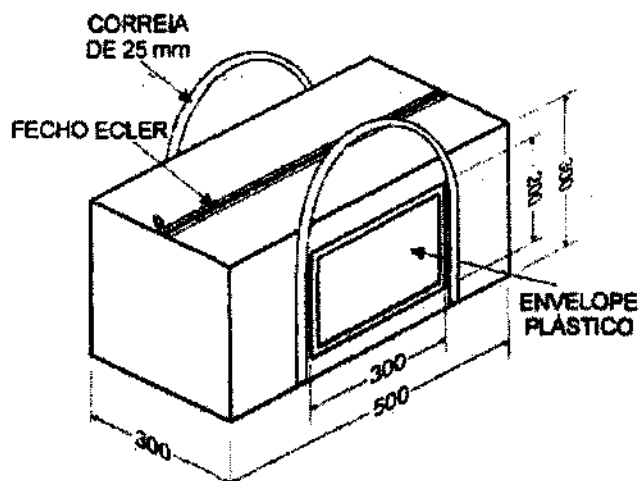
Bolsa para conexões estruturais (conexões e ferragens) (medidas em mm)
